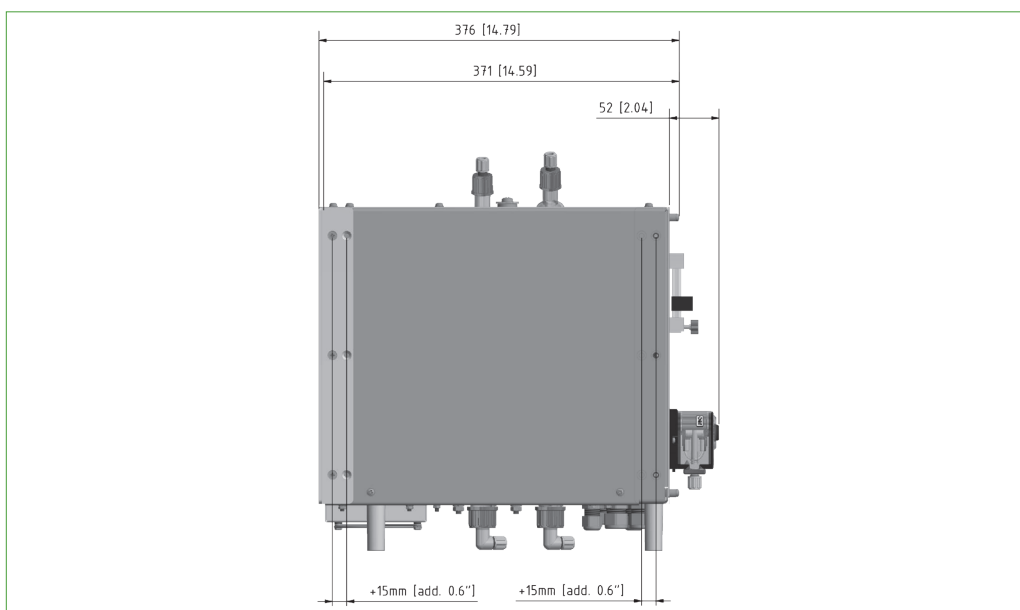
Seitenansicht: Abmessungen incl. optionaler Schlauchpumpen
